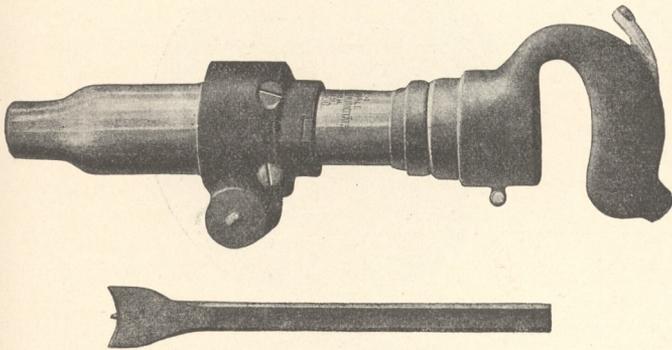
Preßlufthammer mit selbsttätiger Drehvorrichtung des Werkzeuges.
